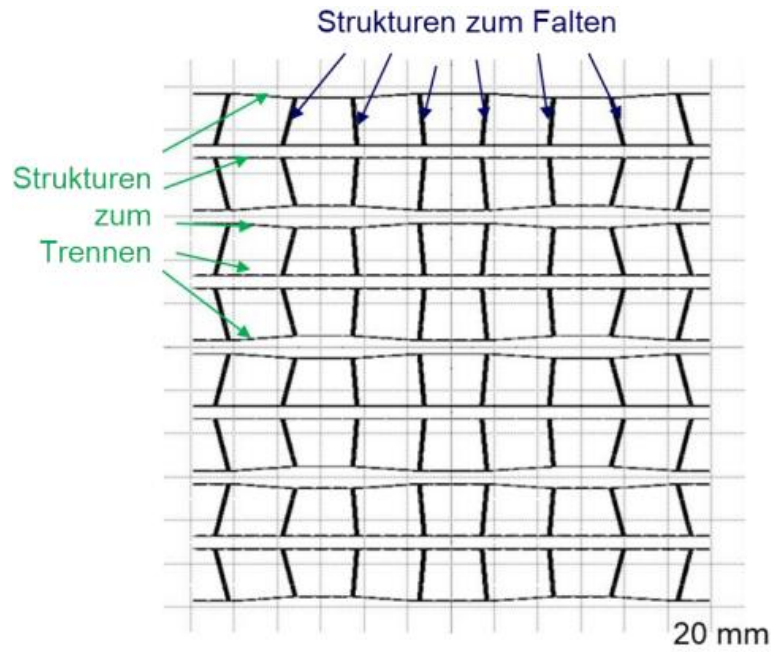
Angepasstes Strukturlayout für die Rolle-zu-Rolle-Bearbeitung
